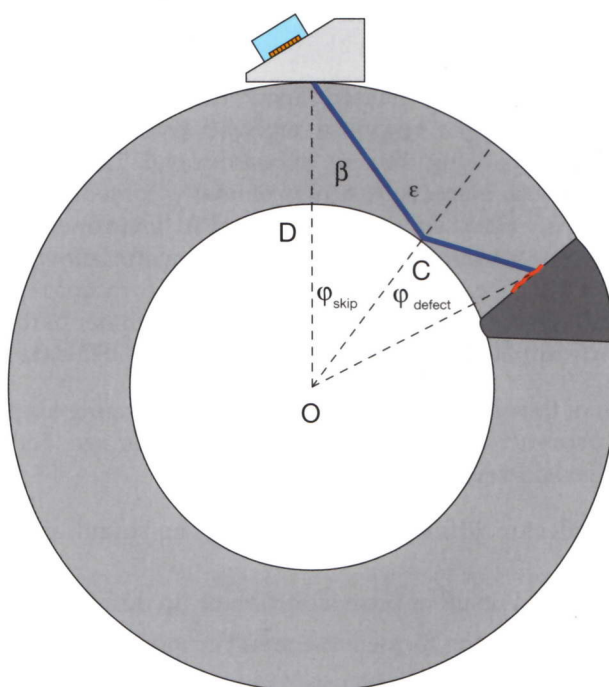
Ультразвуковой контроль продольного сварного шва трубы
